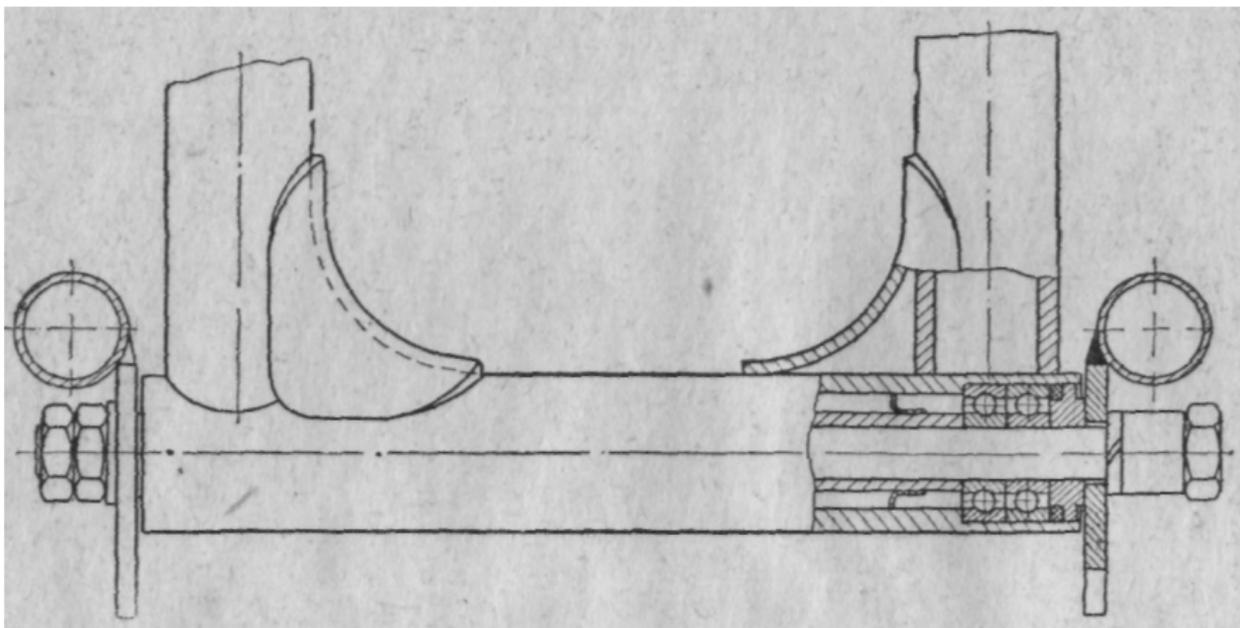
Установка шарикоподшипников в маятниковой вилке.
